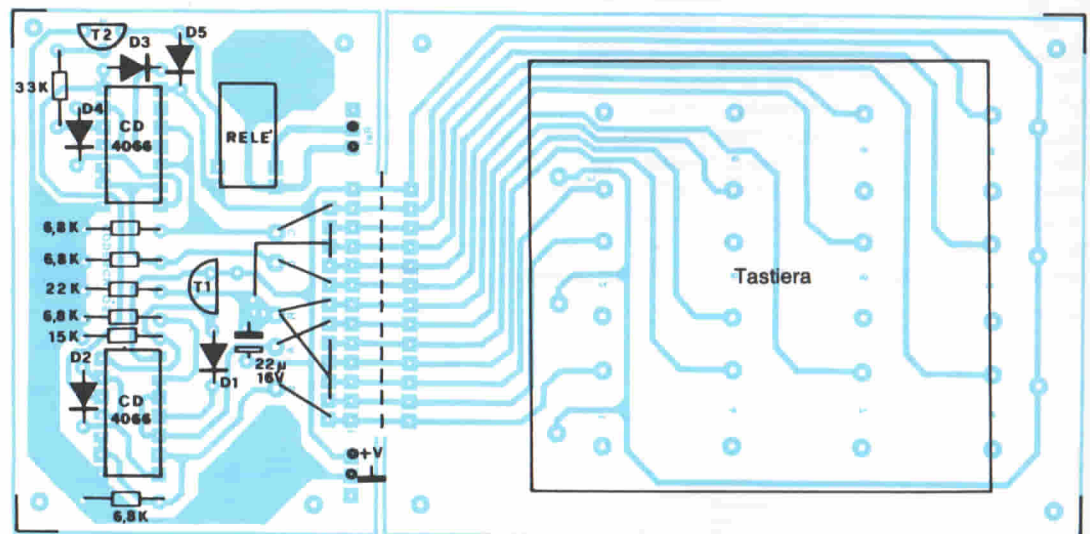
Disposizione dei componenti sui circuiti stampati. Volendo impiegare un commutatore rotativo per "aprire" la serratura, non sarà necessario il circuito stampato di maggiori dimensioni.
